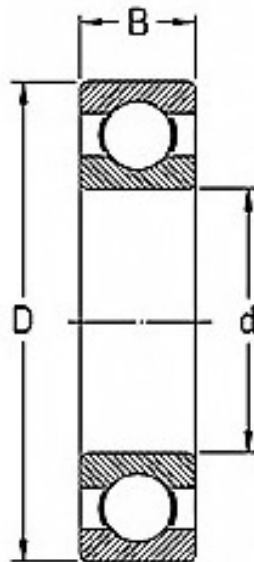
Rodamiento radial. Fuente: Autoría Propia
